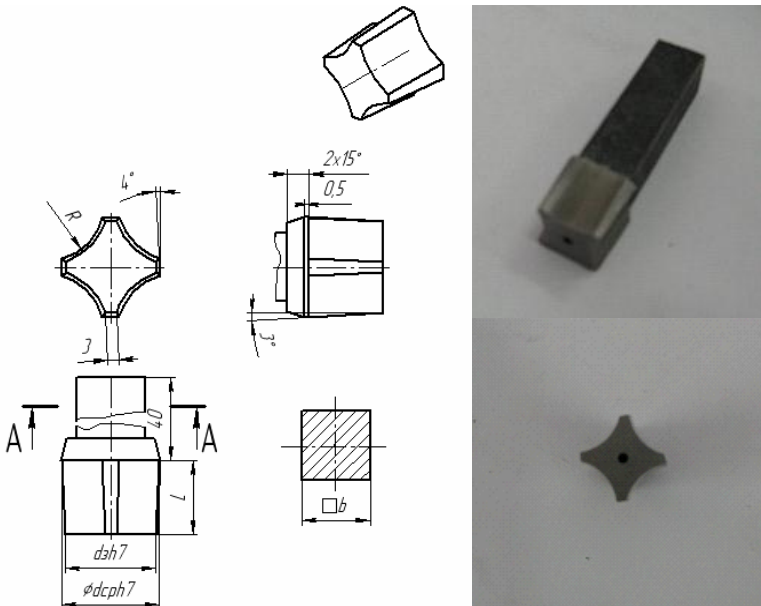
Деформирующий инструмент для глухих отверстий
